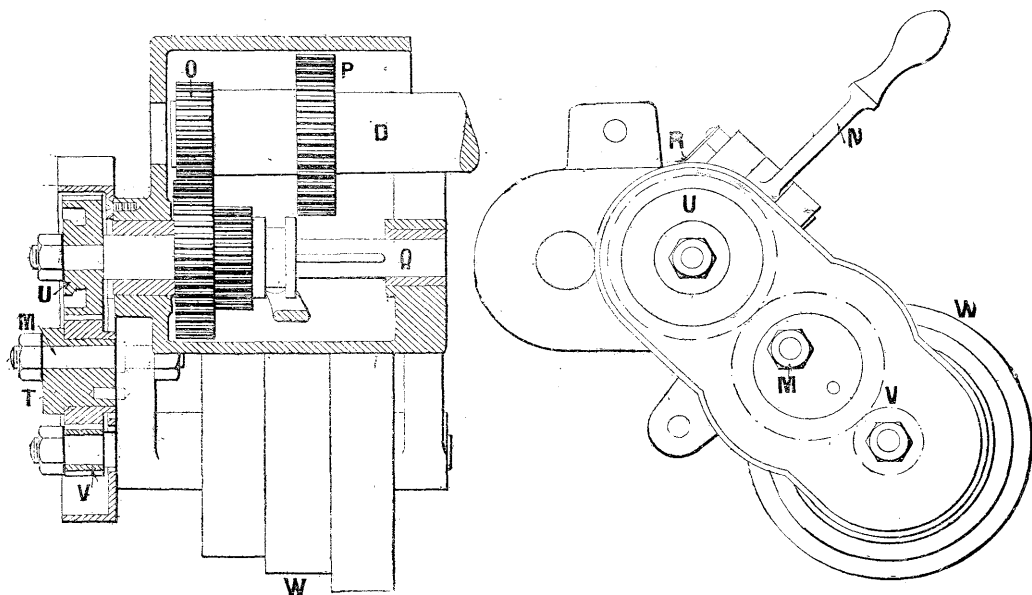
Fraiseuse horizontale de la Cincinnati Milling Machine Company, de Cincinnati (E.-U).
